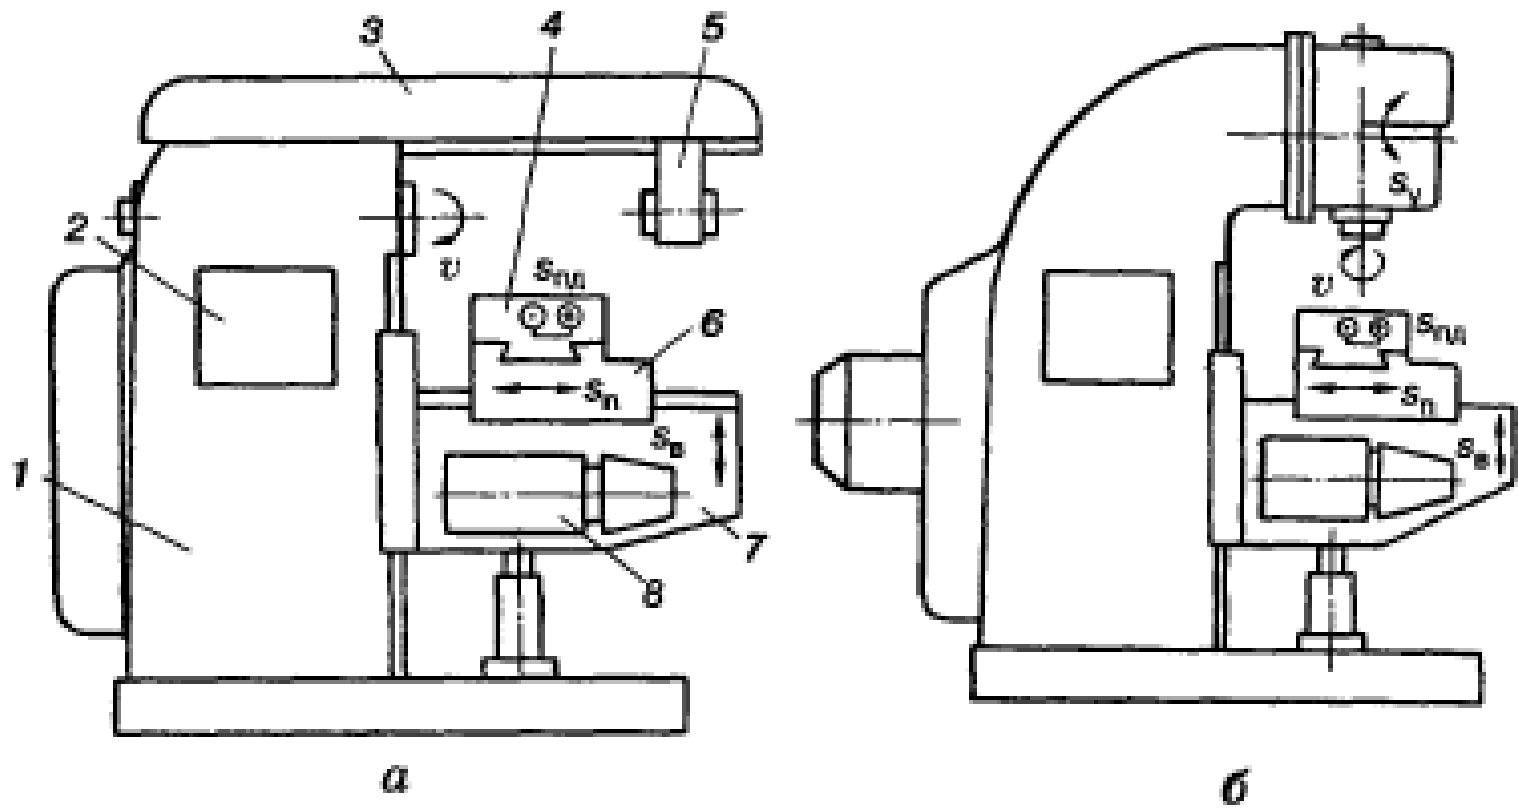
Консольні горизонтально-фрезерний і вертикально-фрезерний верстати
